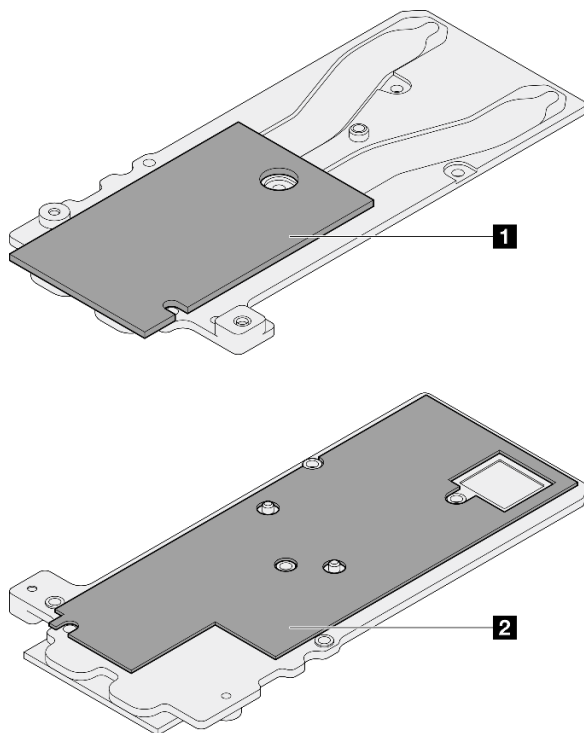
Remplacement des tampons de mastic de la plaque de conduction du module OSFP
